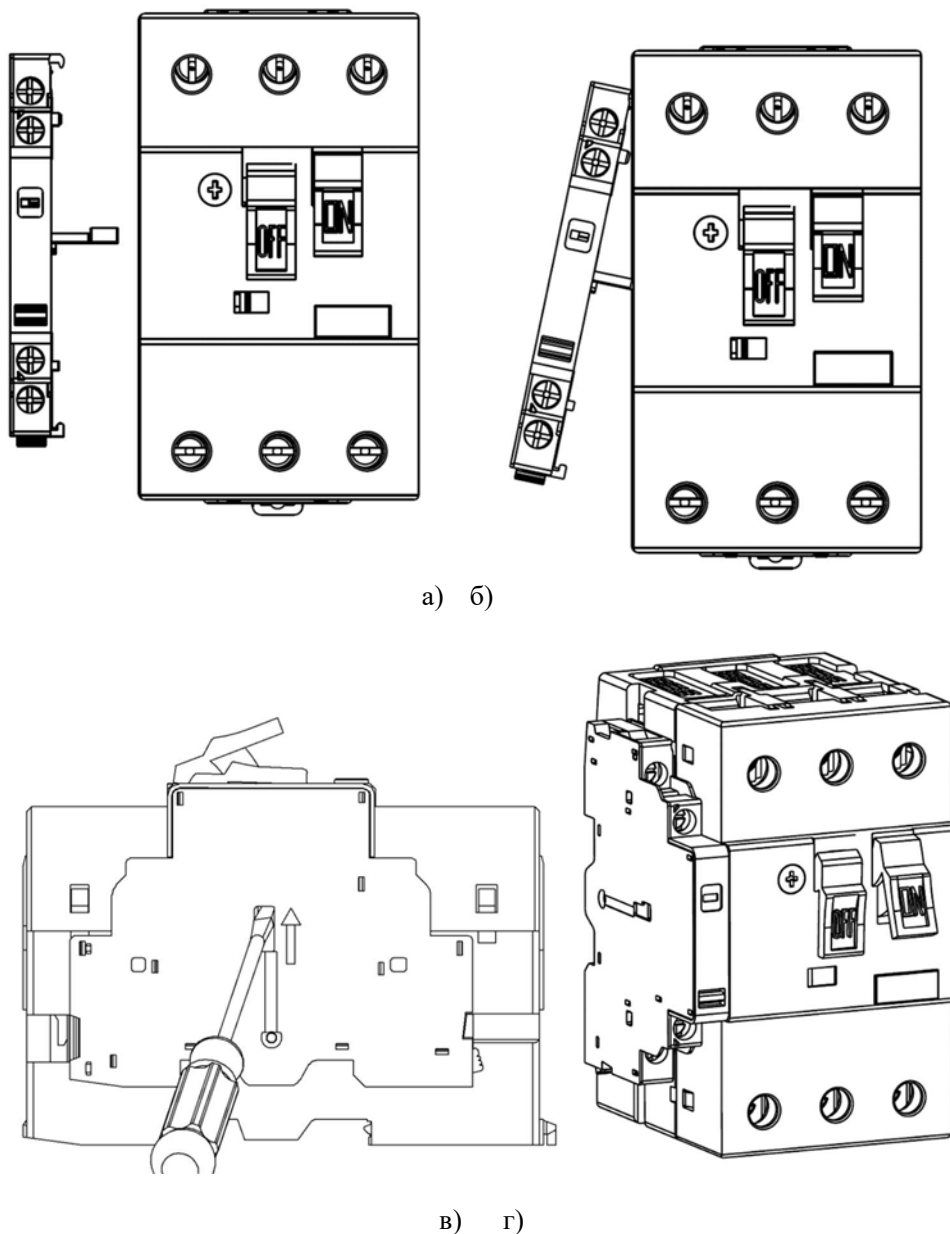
Способ сборки пускателя NS2-AU (80B)
